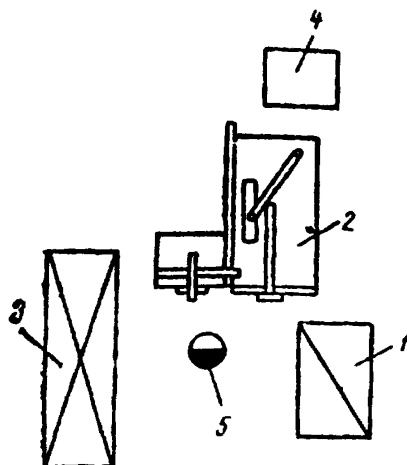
Схема планировки рабочего места станочника-распиловщика по обслуживанию станка Ц6-2:
